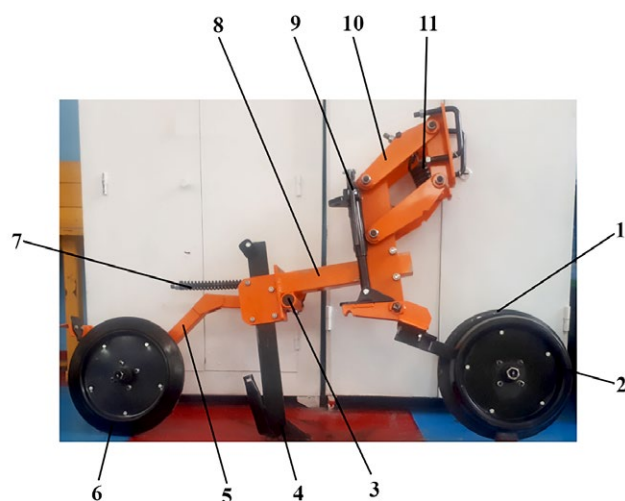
Посевная секция: 1 — прорезной диск; 2 — опорное колесо; 3 — шарнир; 4 — анкерный сошник; 5 — кронштейн прикатывающего колеса; 6 — каток; 7 — регулировочная пружина прикатывающего колеса; 8 — грядиль; 9 — регулятор глубины; 10 — параллелограммный механизм; 11 — регулировочная пружина секции.
